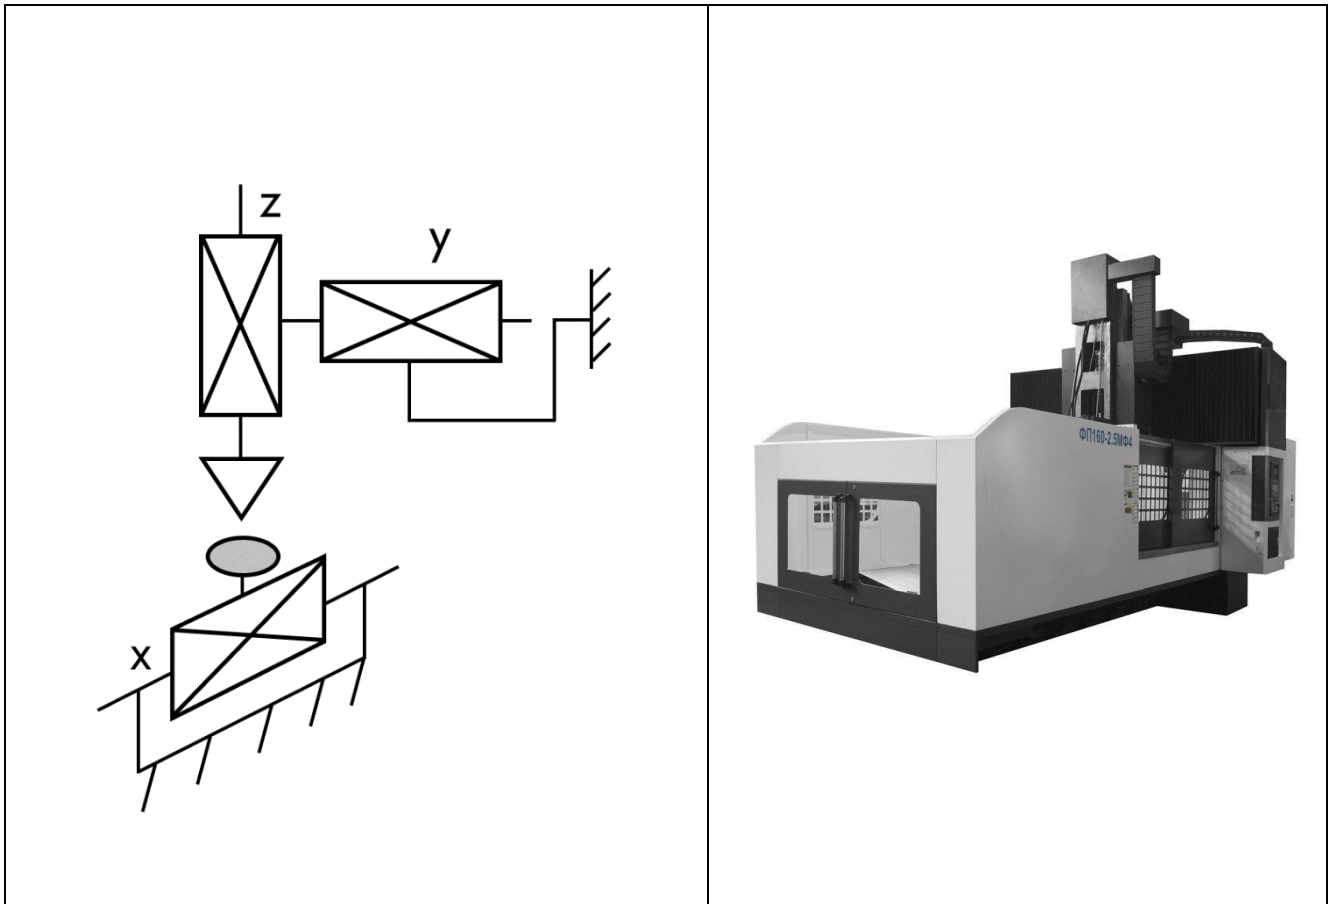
Портальный фрезерный станок ФП160МФ3 (Россия): слева – схема движения, справа – внешний вид
